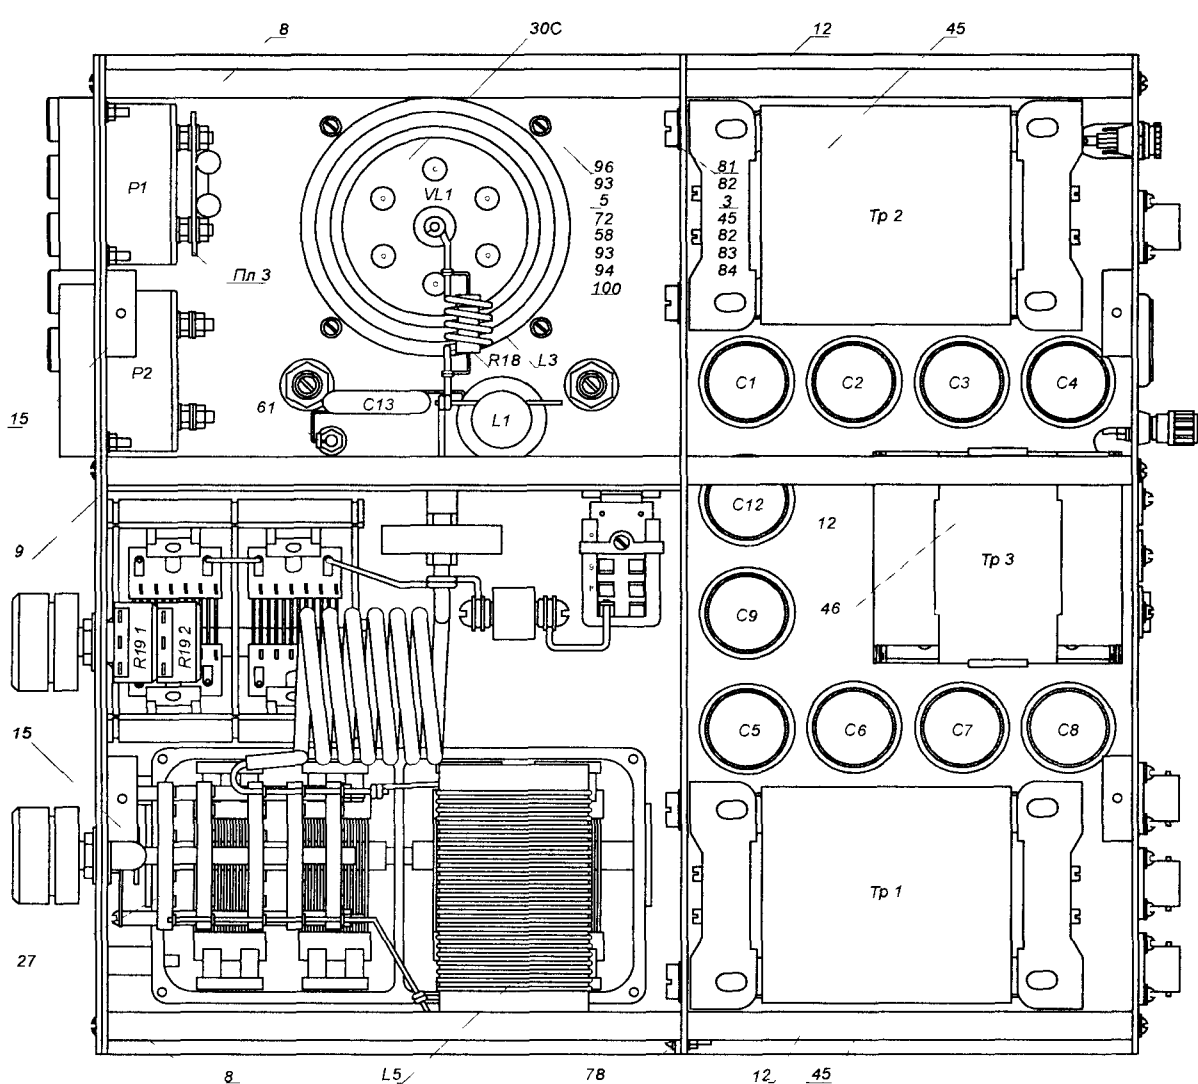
С Сборочный чертеж усилителя ДВА 300С Вид сверху со снятой верхней крышкой
